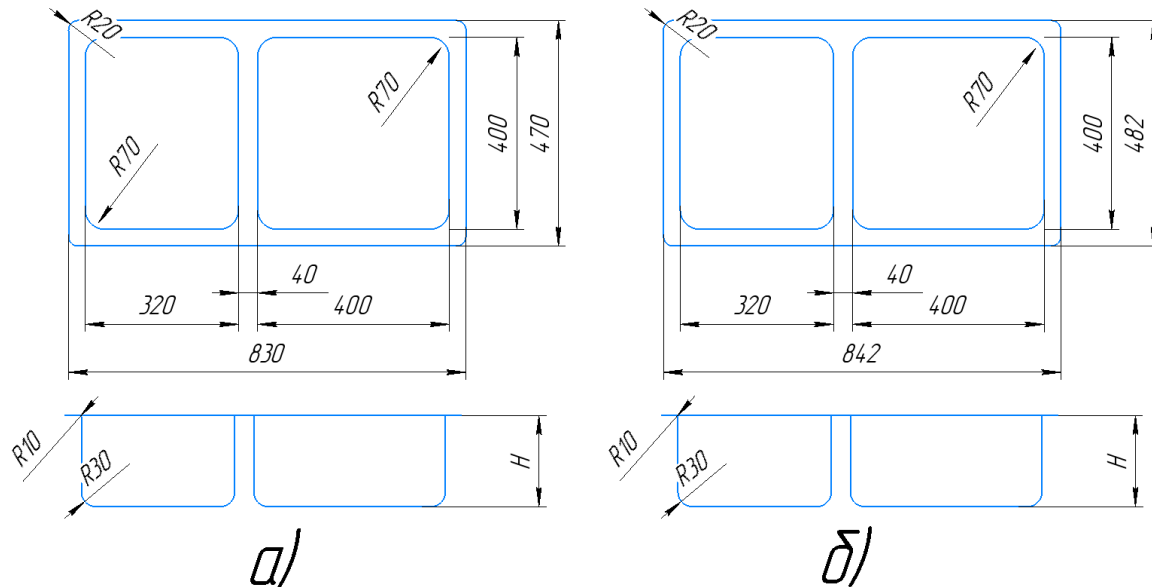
Эскиз детали двойной коробки. а) размеры окончательной детали;
